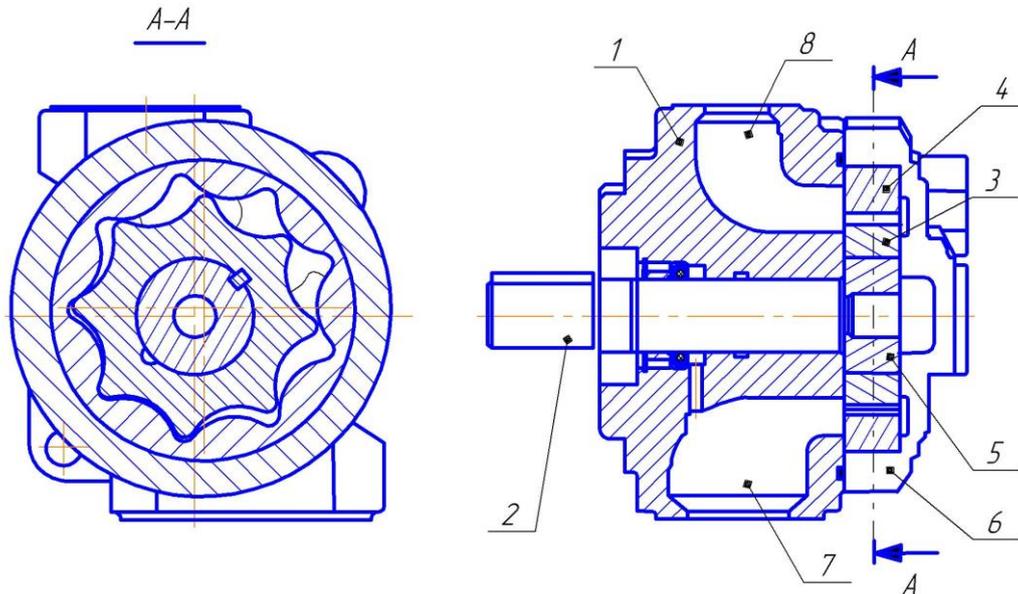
Героторный насос типа PGZ: 1 – корпус; 2 – вал; 3 – внутренний охватываемый ротор; 4 – внешний охватывающий ротор; 5 – соединительная муфта; 6 – крышка; 7 – входной канал; 8 – выходной канал.
